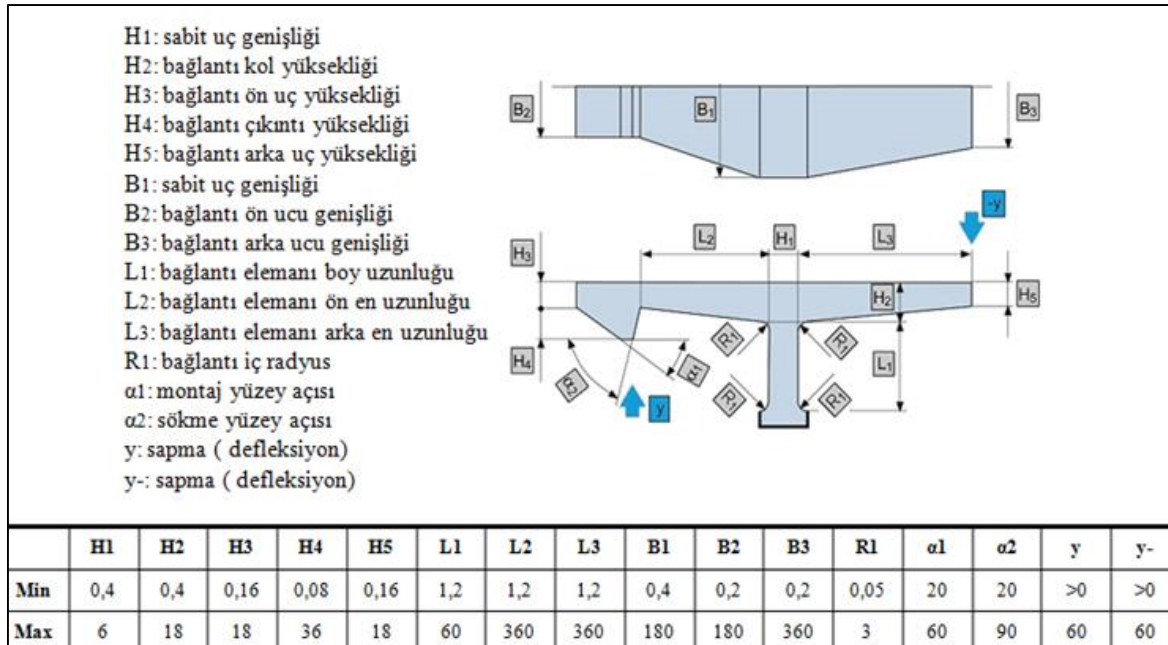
I tipi esneyerek kilitlenen bağlantı elemanının boyutlandırılması [42]
